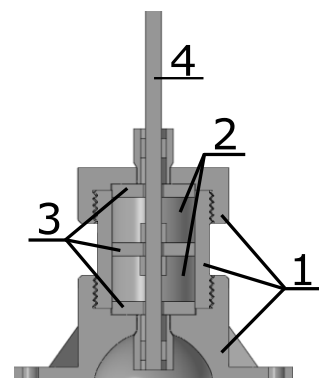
Конструкция демпфера: 1 – пластиковый корпус, 2 – опытный образец (эластомер), 3 – неодимовые магниты, 4 – направляющий стержень
